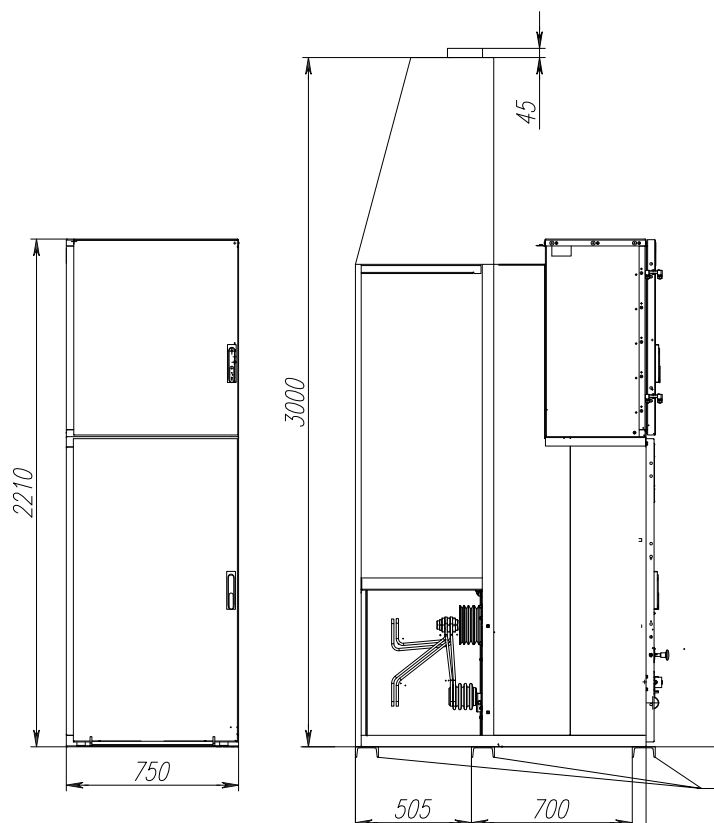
Общий вид и габаритные размеры шкафа К-128 кабельного ввода на номинальные токи до 1600 А (ввод сверху шкафа)
